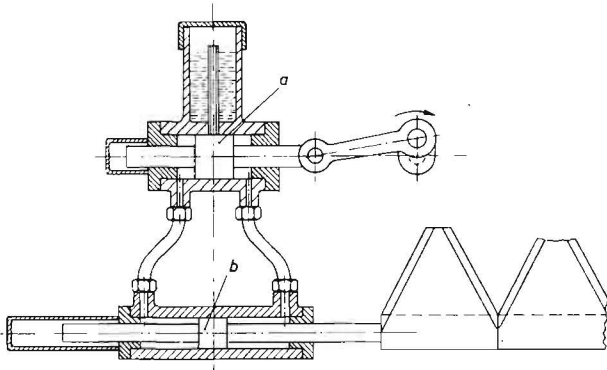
Schwingtrieb mit doppeltwirkender Kolbenpumpe (hydraulisches Gestänge)
